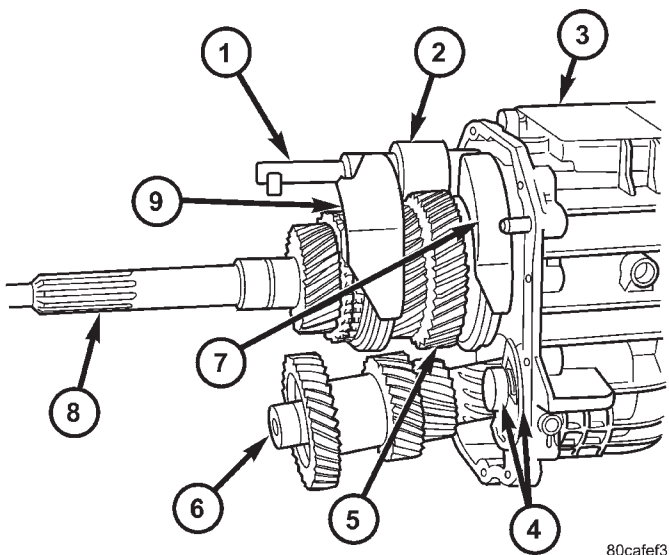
TREN DE ENGRANAJES Y COMPONENTES DE CAMBIOS
